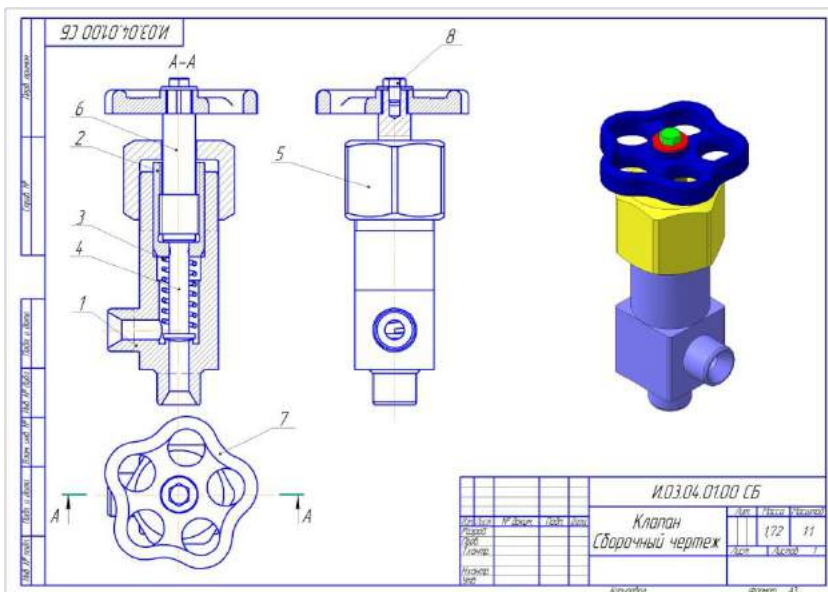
Сборочный чертёж и трехмерная модель сборочного узла
